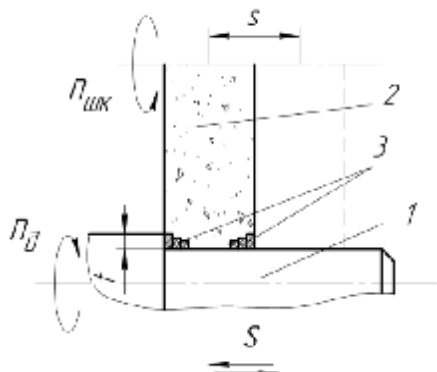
Багатопрохідне шліфування периферією циліндричного круга
